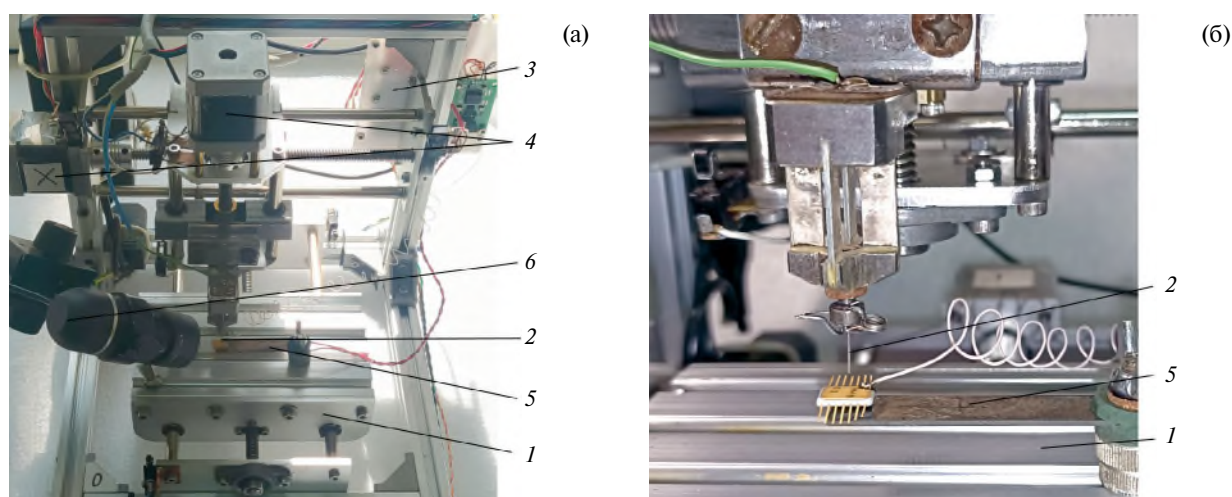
Схема маркиратора: а – общий вид маркиратора, б – детальный вид узла иглы:
